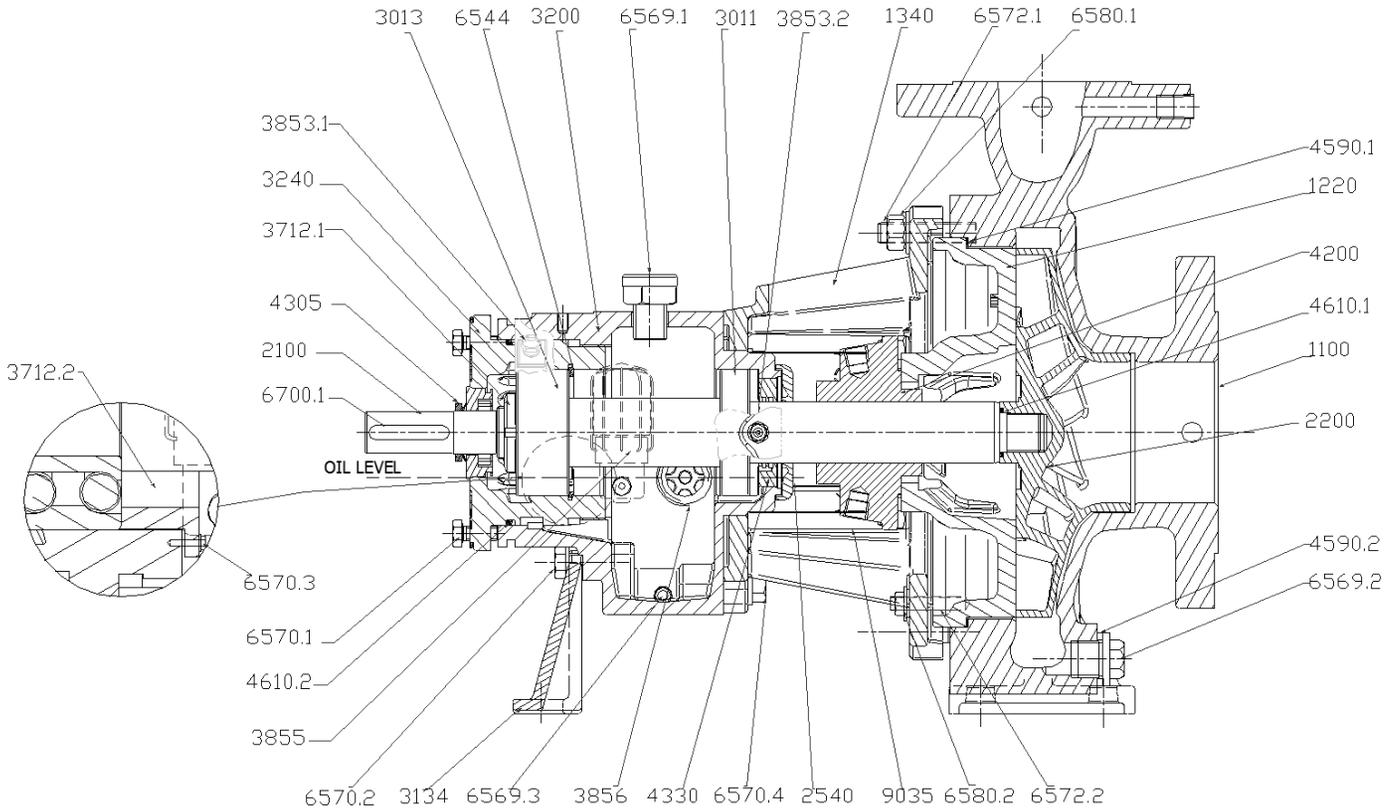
Desenho de corte da bomba do rotor de palheta reversa
